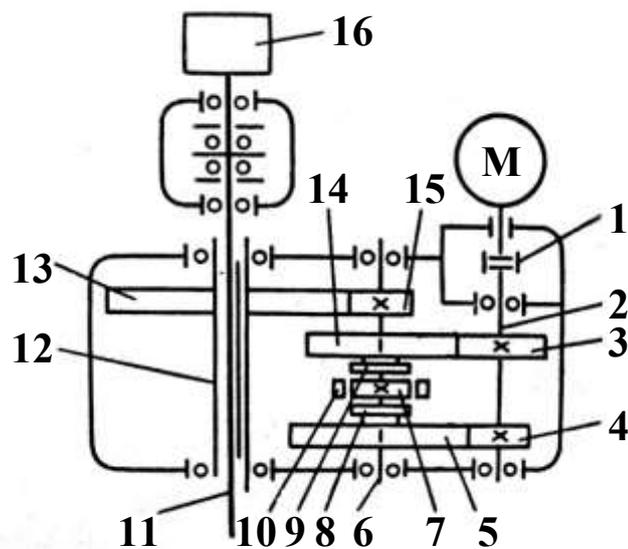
Кинематическая схема бурового станка установки БГА-2М
